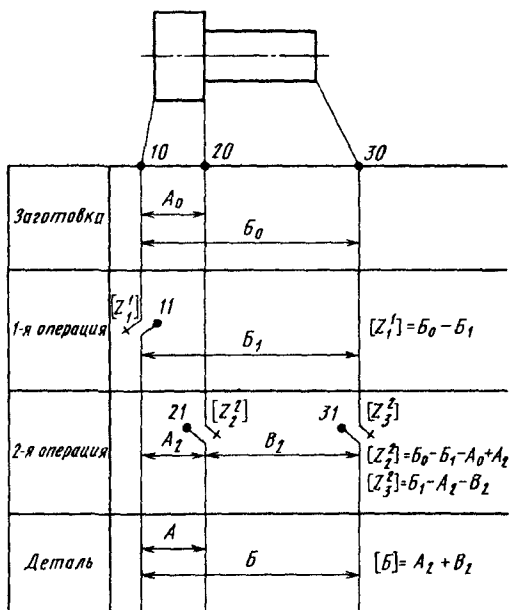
Схема размерного анализа технологического процесса изготовления валика
